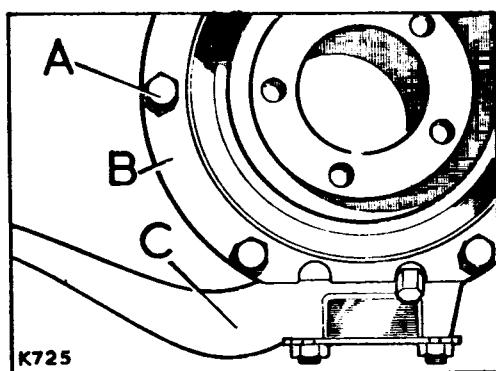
Posición del tornillo de ajuste del tope de dirección.
